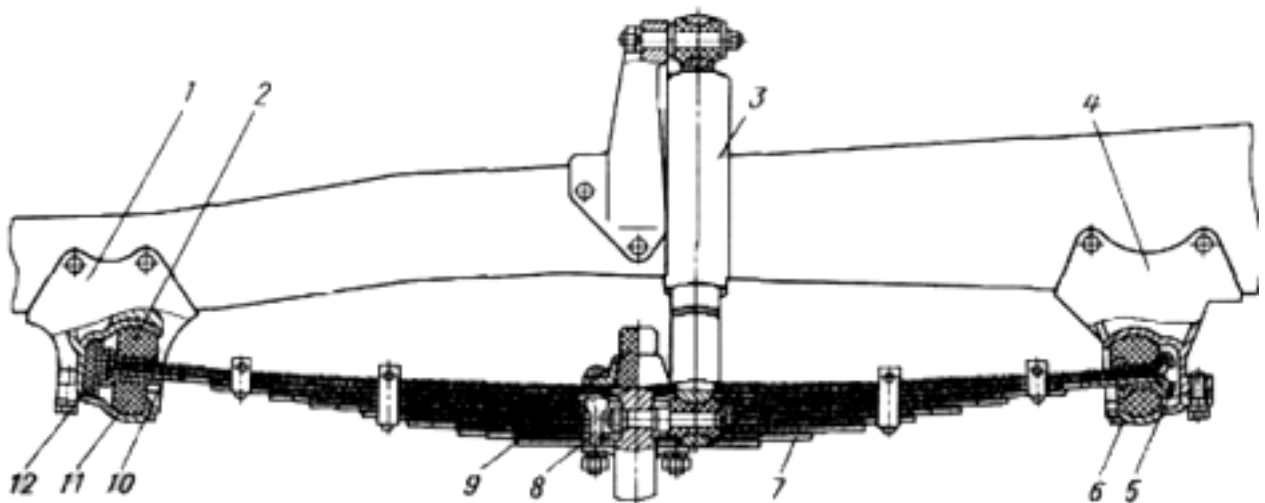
Передняя подвеска грузового автомобиля ГАЗ-53А
